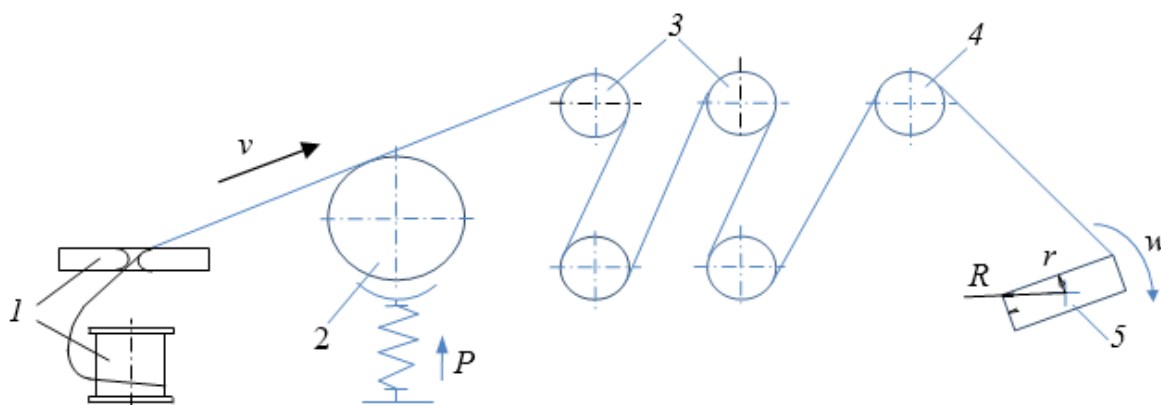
Кинематическая схема устройства для изготовления обмоток
